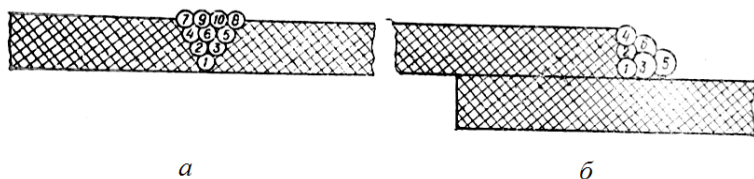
Последовательность укладки прутков в сварной шов:
